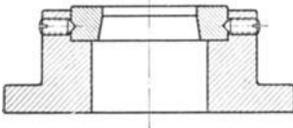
Befestigung der Schnittplatte durch Druckschrauben.
